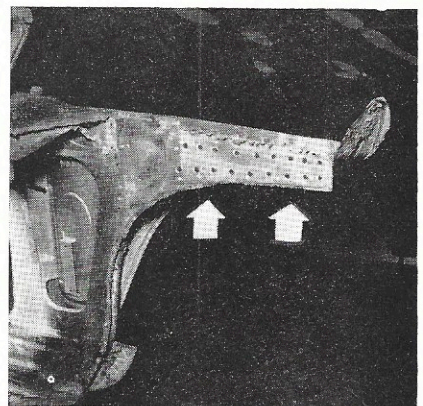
Percer les points de soudure électrique fixant le renfort d'armature sur doublure d'aile avant assemblée.
